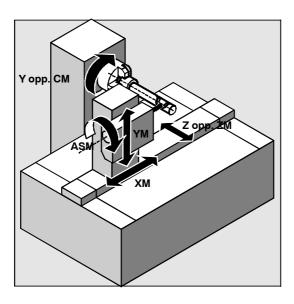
Cinematica di macchina con asse Y (YM) di macchina
